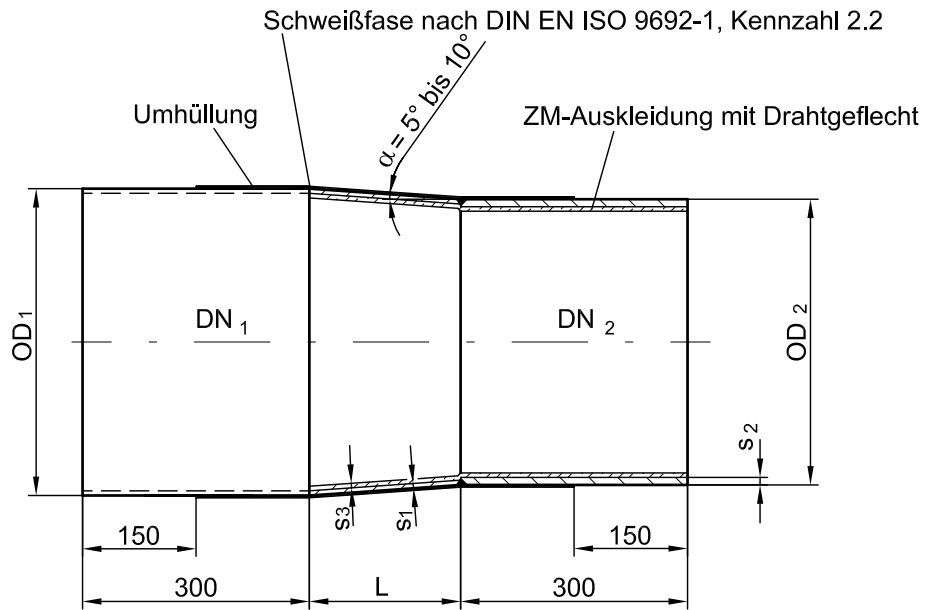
Reduzierungen von Stahl- auf Gussrohr (R-Stücke) – Ausführung G
